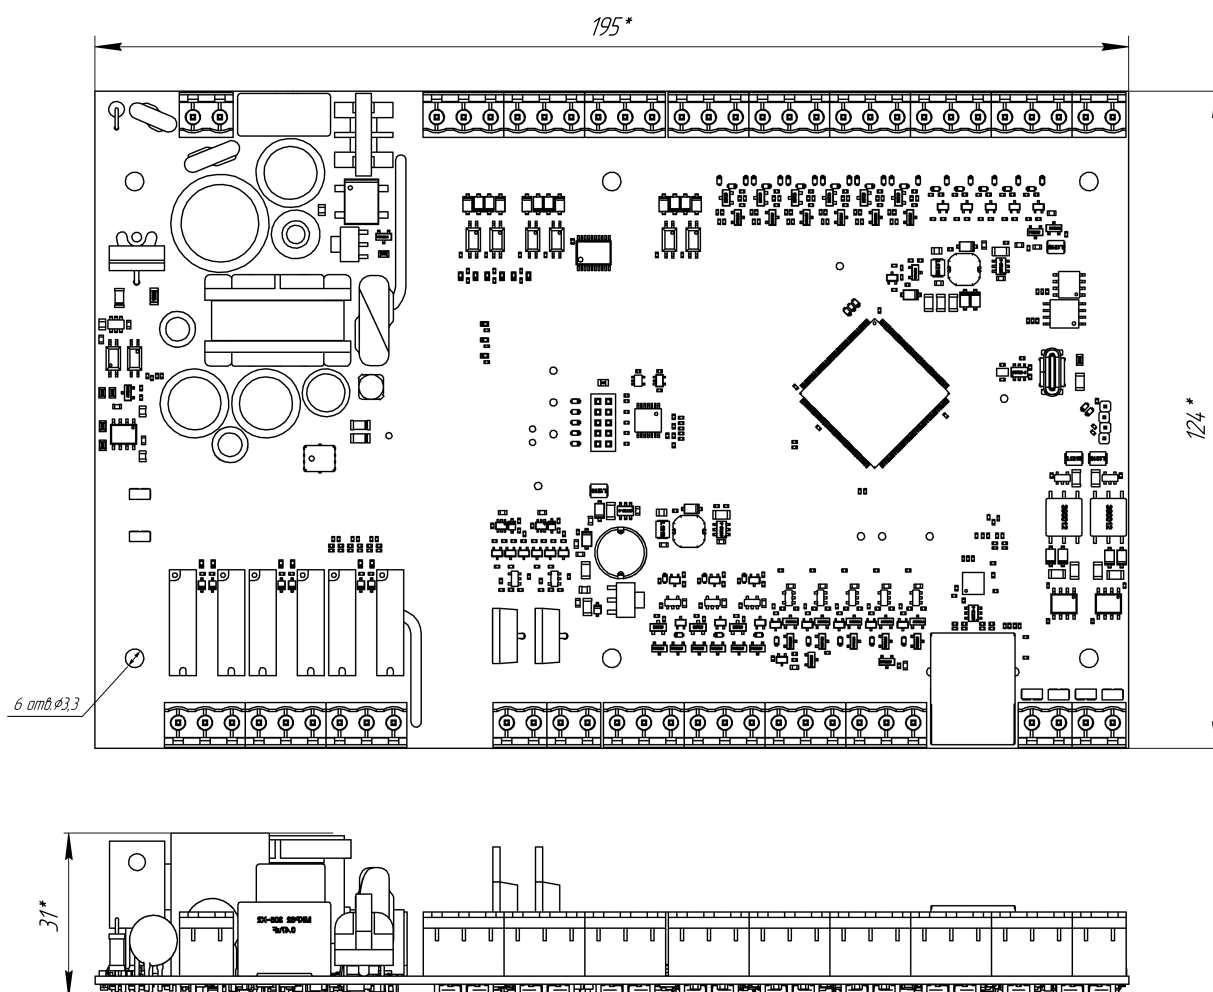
Габаритные и установочные размеры ОВК–П–230
